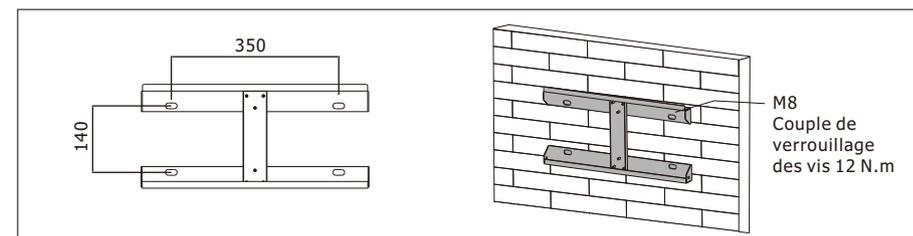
Installation de la plaque de suspension de l'onduleur
